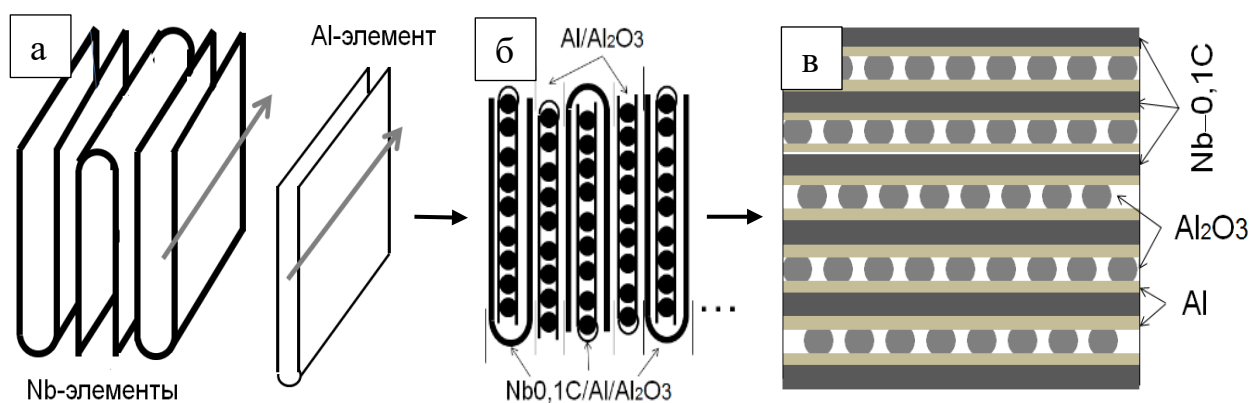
Nb – и Al – элементы U-образной или «книжной» формы (а), схема сборки заготовки (б), заготовка после сборки (в). Стрелками показано направление прокатки фольг из сплава $Nb - 0.1C$ и алюминия.
